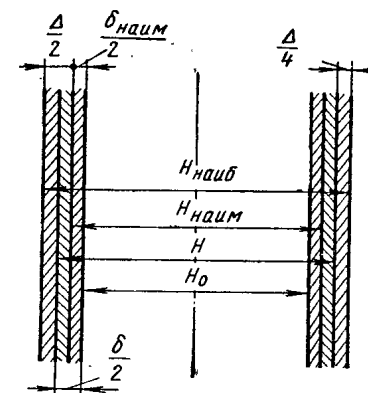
Схема расположения припусков и допусков на наружный размер детали (ГОСТ 7062—67):
